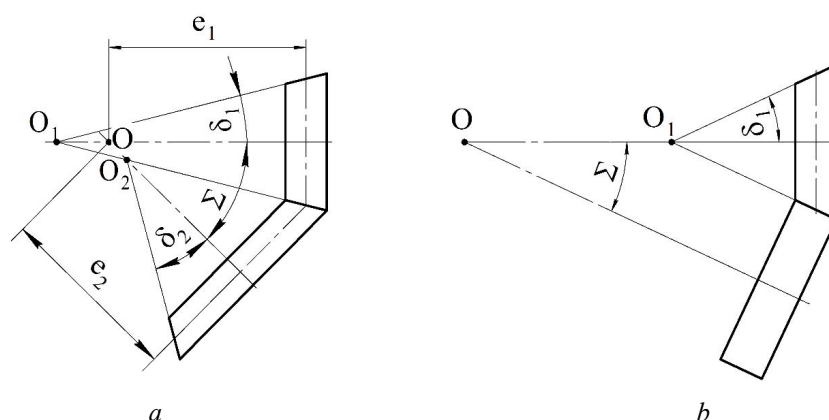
Конические зубчатые передачи из ЭКК: *a* – из двух ЭКК; *b* – из ЭКК и цилиндрического колеса
